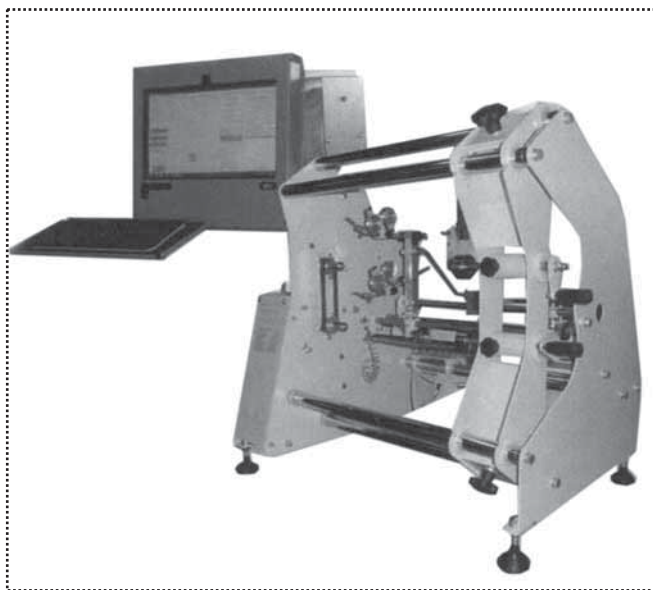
Двухвальный намоточный станок СНС-2.0-300-2В
